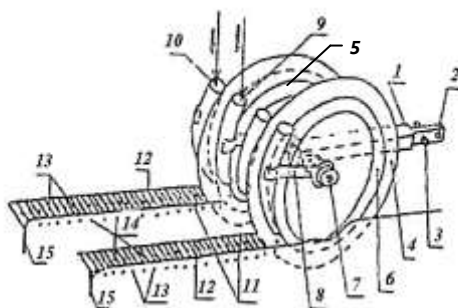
Технический процесс работы комбинированного двухдискового сошника с разновеликими ребордами: 1 – корпус; 2 – отверстие; 3 – болт; 4 – диск; 5, 6 – реборды-бороздкообразователи-уплотнители; 7 – ось; 8 – пластина; 9, 10 – семянаправители; 11, 12 – бороздки; 13, 14 – семена трав и зерновых; 15 – щели
